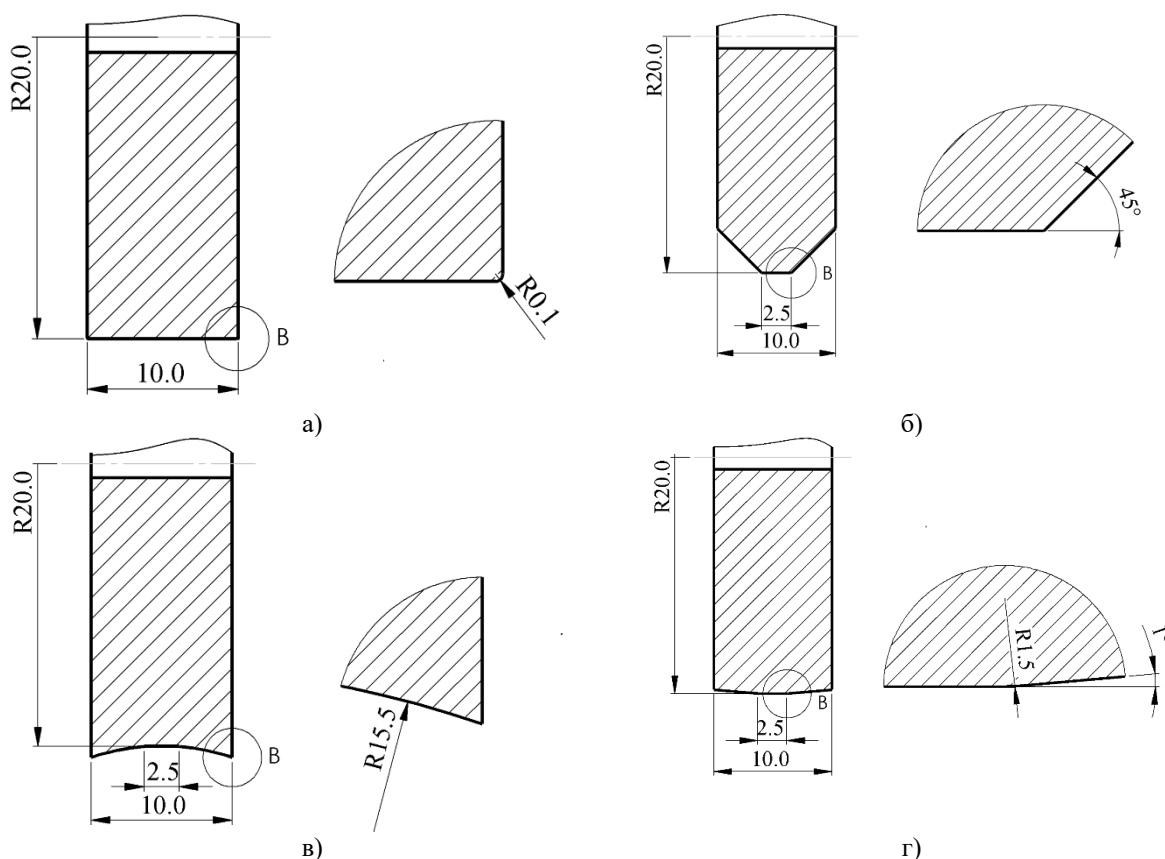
Конструктивные варианты рабочего профиля деформирующего инструмента: а – базовый цилиндрический ролик (вариант I); б – ролик с фаской 45° (вариант II); в – ролик с поднутрением профиля (вариант III); г – модифицированный ролик с радиусным переходом (вариант IV)
